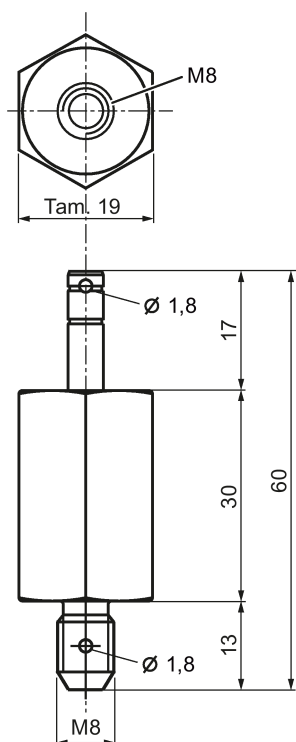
Desenho de dimensões do suporte de substituição rápida 6GT2690-0AH00
